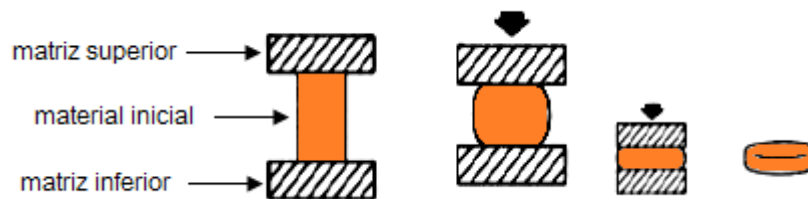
Forjado a dado abierto. Fuente: Fundamentos de Manufactura Moderna
